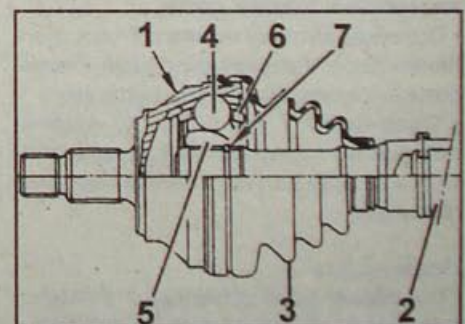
Шарнир равных угловых скоростей с наружной стороны приводного вала:
